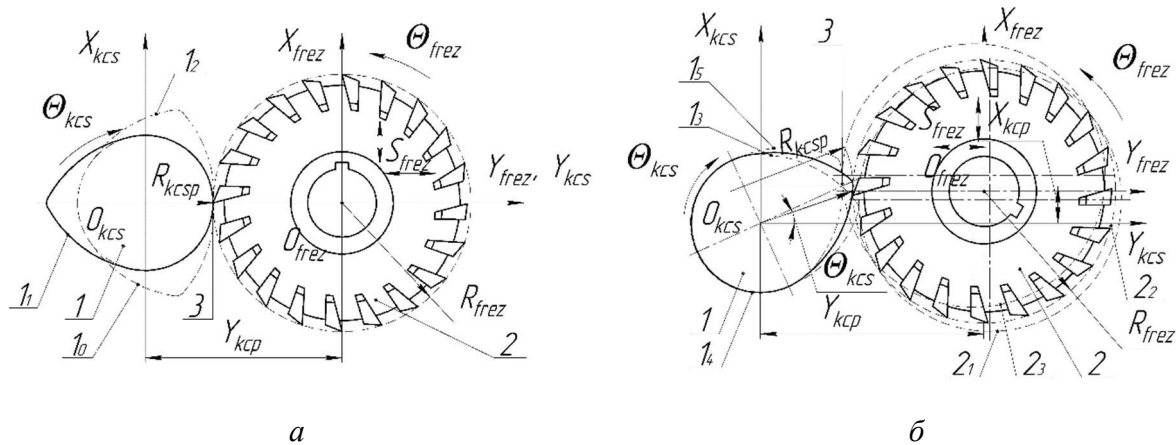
Схема фрезерування криволінійної поверхні кулачка
